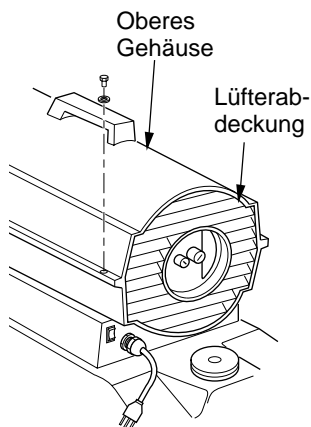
Entfernen des oberen Gehäuses, GK20 Modell
